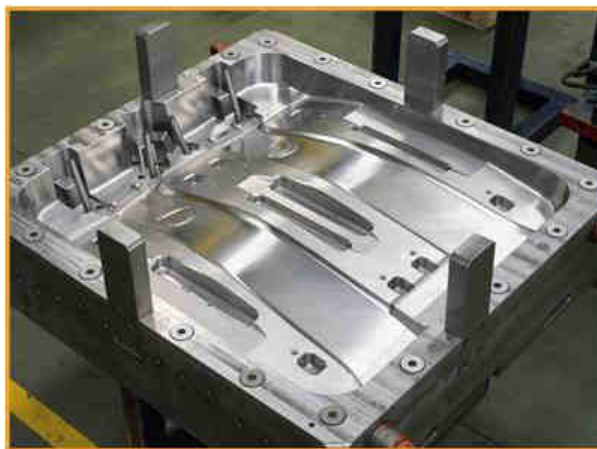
Molde de moldeo rotacional fabricado en aluminio. Versaplast.
